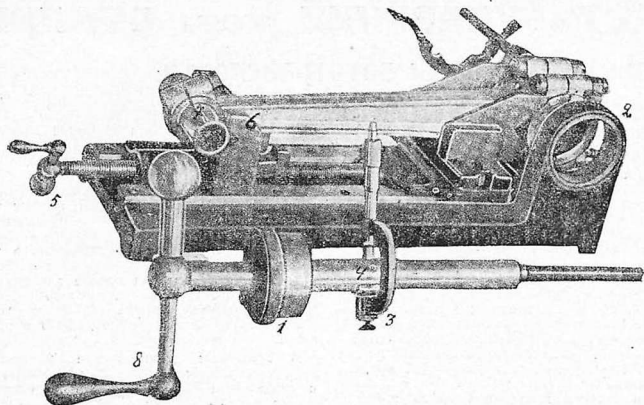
Приспособление дает возможность обработки и шатунных подшипников
